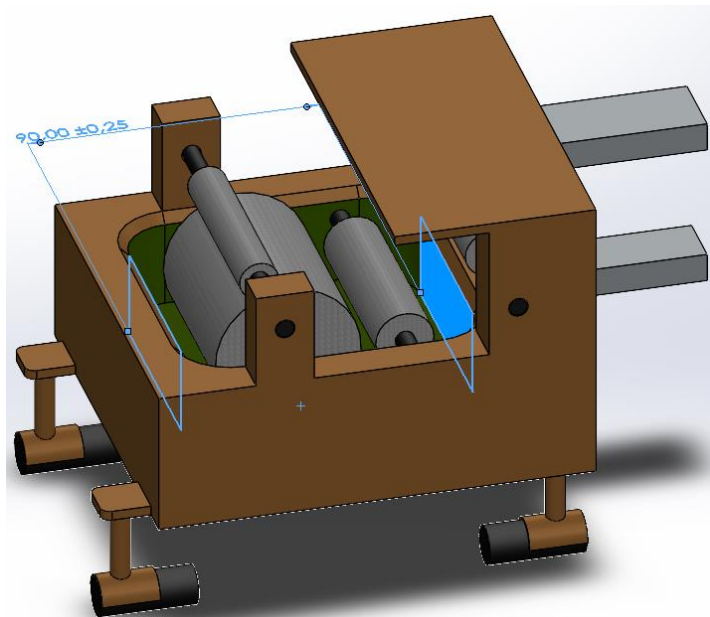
diseño de carrito móvil con dimensión tolva de resina. Autor
